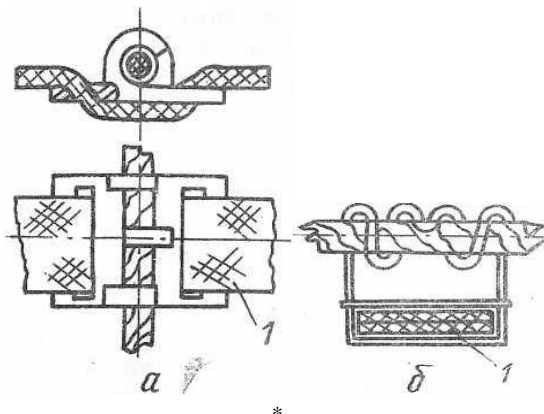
Ограничители отбрасывания (а — фрезерованный, б — проволочный):
